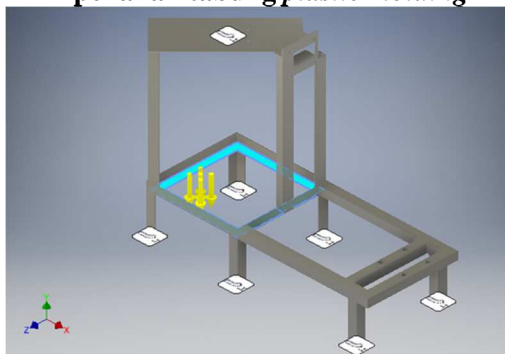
Hasil *assembly mesin plastic molding* (Dokumentasi, 2021).
